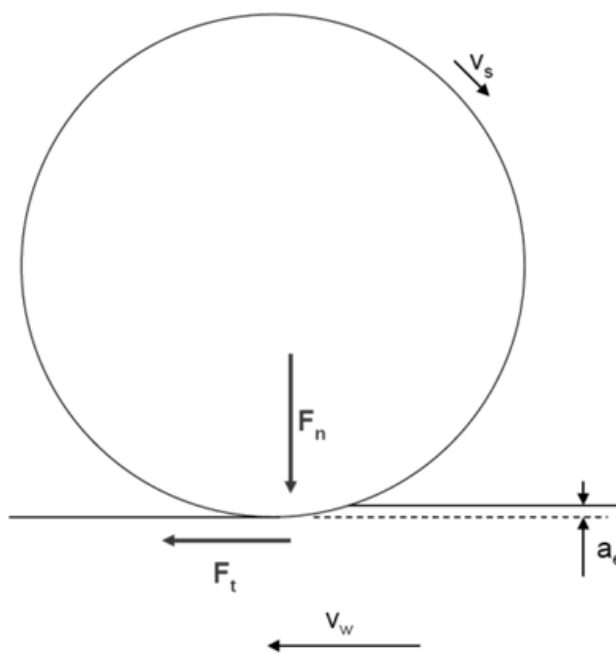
Descomposición de fuerzas en rectificado cilíndrico.
